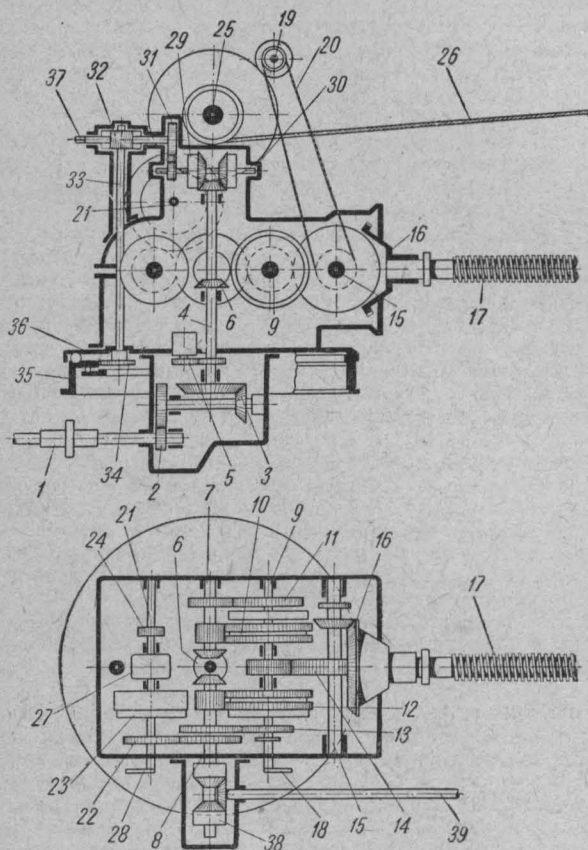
Схема устройства башенного механизма автомехлестницы.
